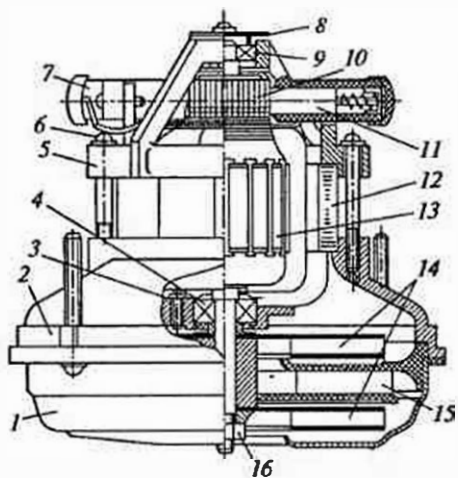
Конструкция воздуховсасывающего агрегата
